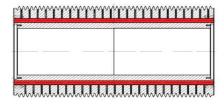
Detalhe em corte Furos Longitudinais. Fonte: simisa-empral, 2018
